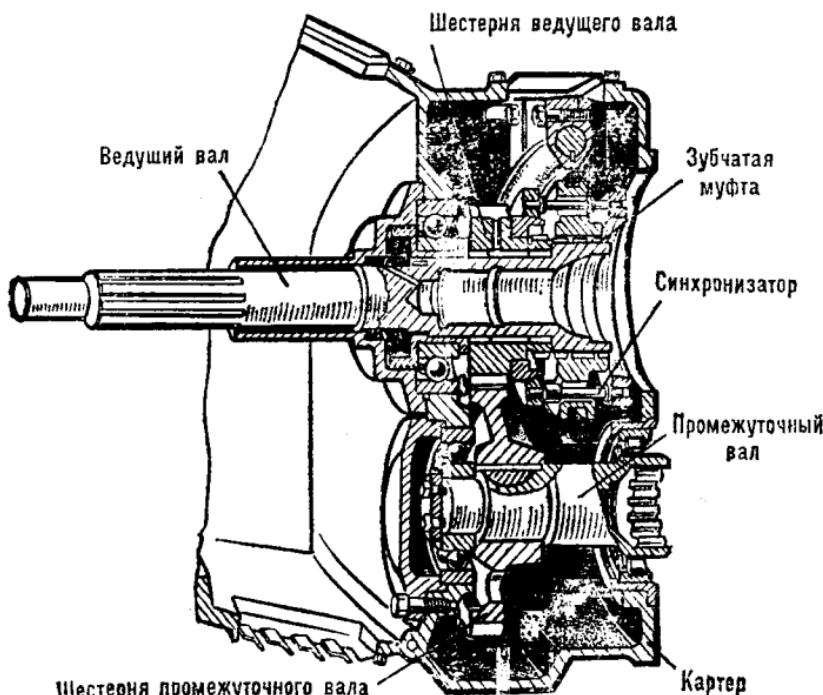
Делитель коробки передач автомобиля КамАЗ
